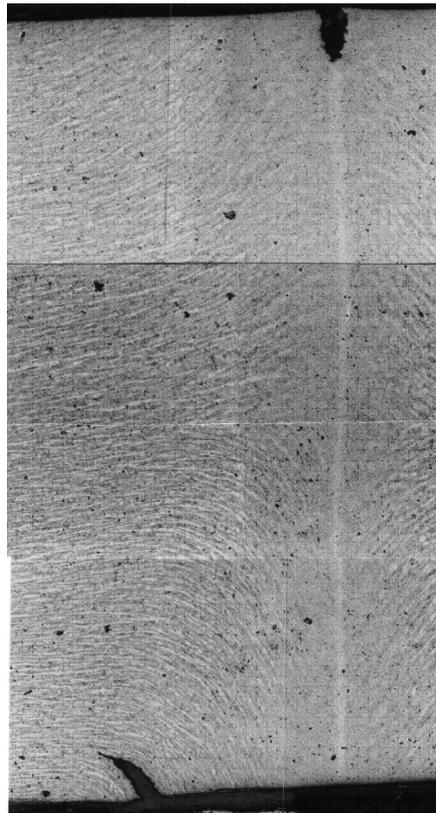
Corte transversal de una soldadura ERW de baja frecuencia (X25) [13]
